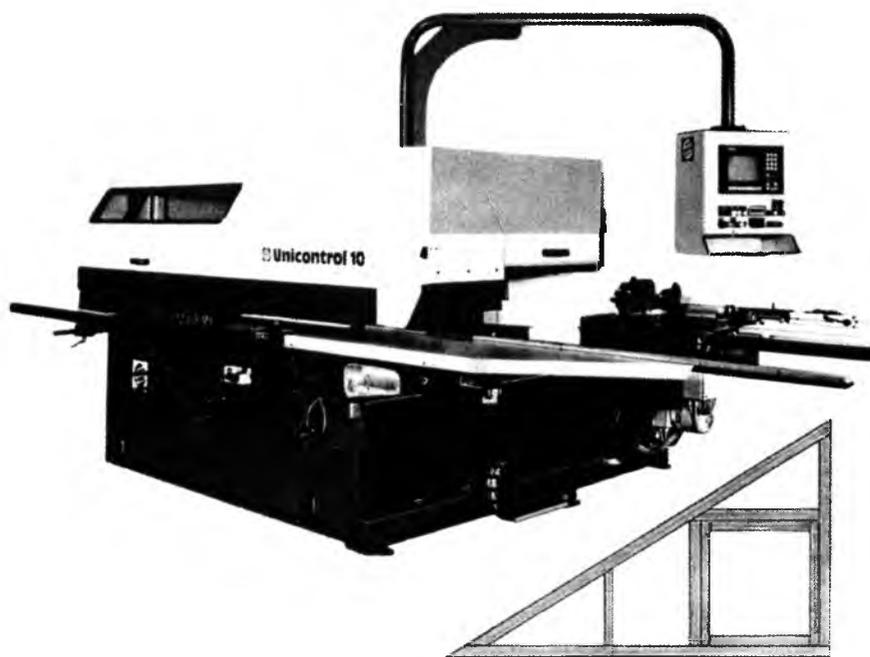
Обрабатывающий центр Unicontrol 10 для изготовления деревянных окон и дверей
